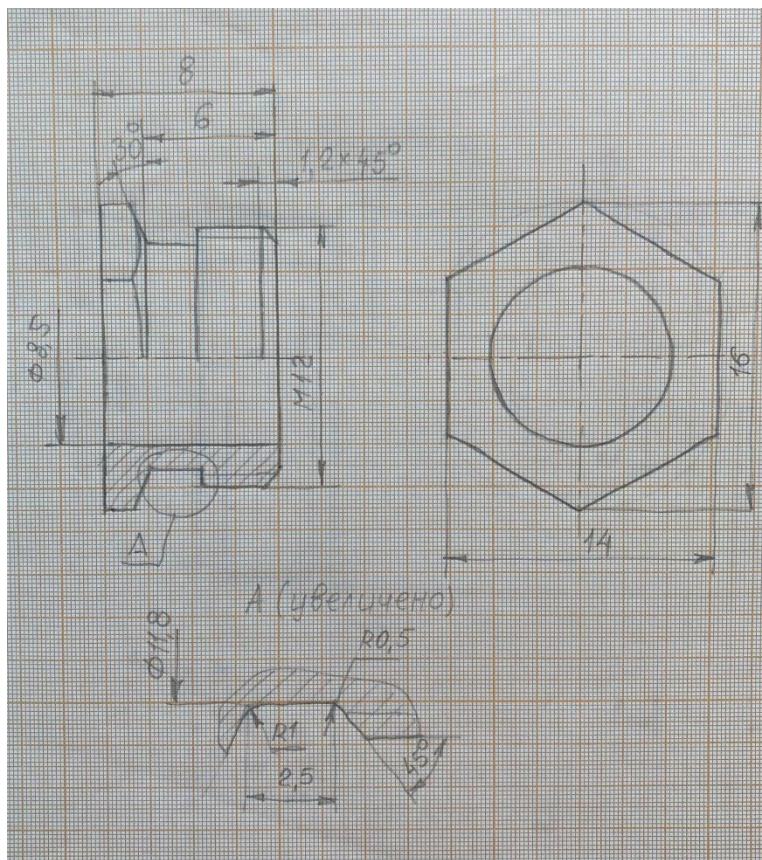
Пример чертежа втулки с резьбой в эскизном оформлении
